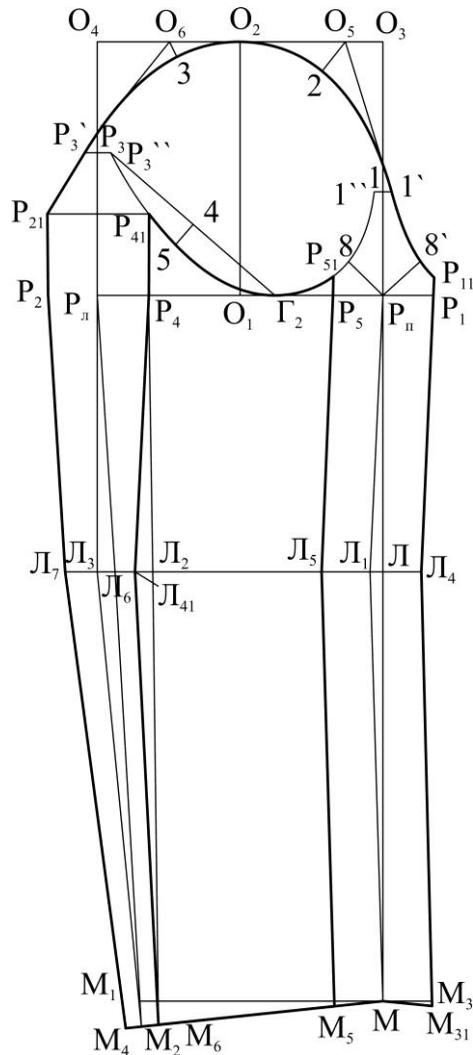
Чертеж базовой конструкции рукава женского жакета
